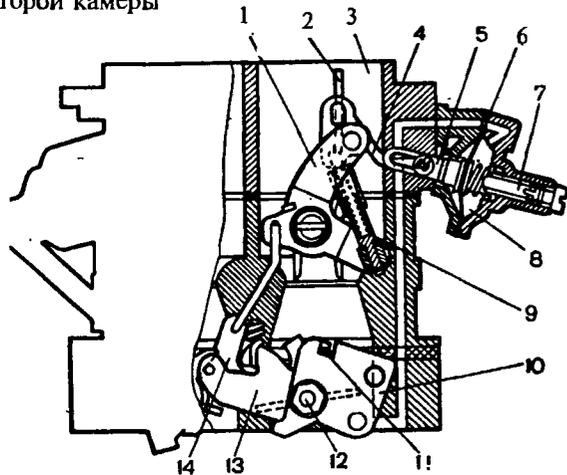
Схема пускового устройства карбюратора 2107-1107010: 1 - рычаг управления воздушной заслонкой; 2 - воздушная заслонка; 3 - воздушный патрубок первой камеры; 4 - тяга; 5 - шток пускового устройства; 6 - диафрагма; 7 - регулировочный винт; 8 - полость, сообщающаяся с задрасельным пространством; 9 - телескопическая тяга; 10 - рычаг привода дроссельных заслонок; 11 - сектор (усик); 12 - ось дроссельной заслонки первой камеры; 13 - рычаг на оси дроссельной заслонки первой камеры; 14 - рычаг, связанный с воздушной заслонкой
